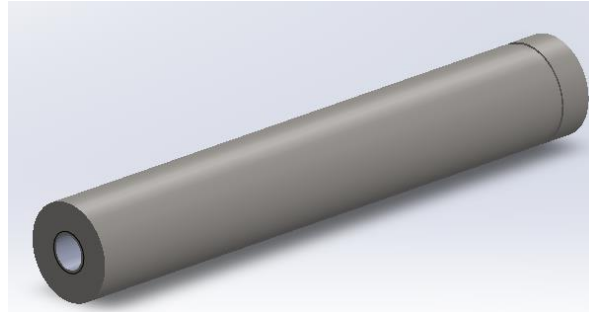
Vista de soldado de pieza N°15 (Fuente 106)
